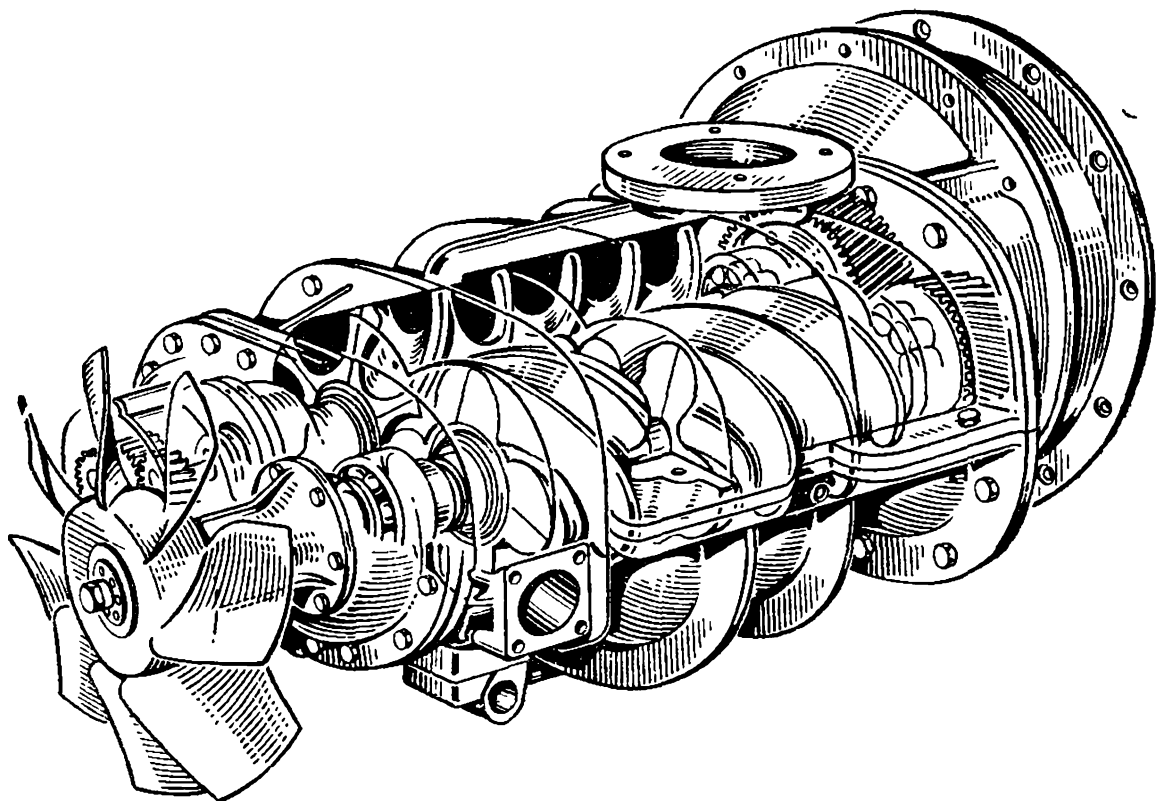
Однокорпусный двухступенчатый компрессор (фирма Атлас Копко, Швеция)
